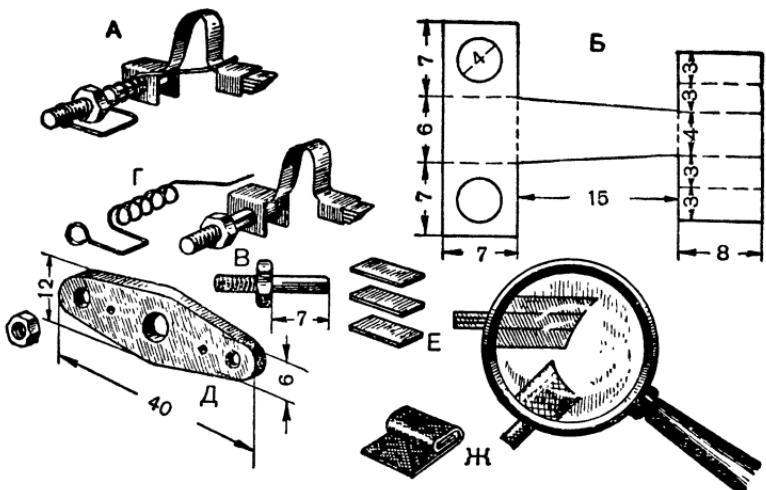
Наборные и брусковые щетки: А — общий вид щетки; Б — развертка щеткодержателя; В — укороченная ножка от штепсельной вилки; Г — спиральная пружина; Д — пластина щеткодержателя; Е — заготовка наборной щетки; Ж — заготовка брусковой щетки.
